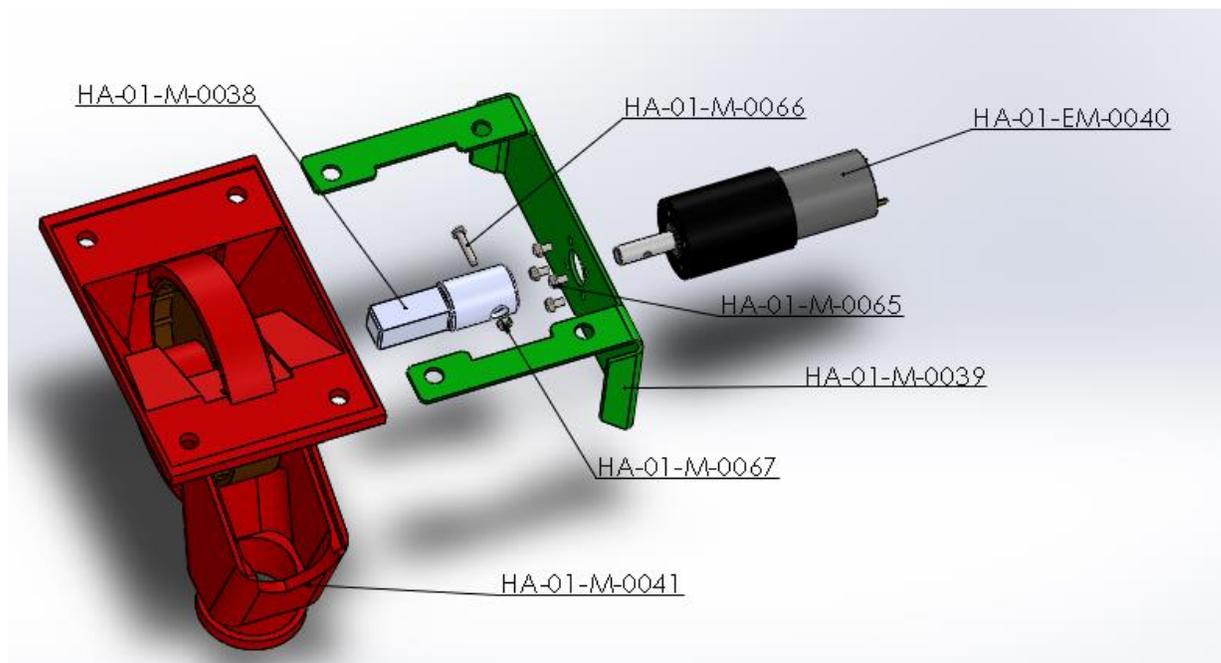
Vista explosionada del montaje del motorreductor
